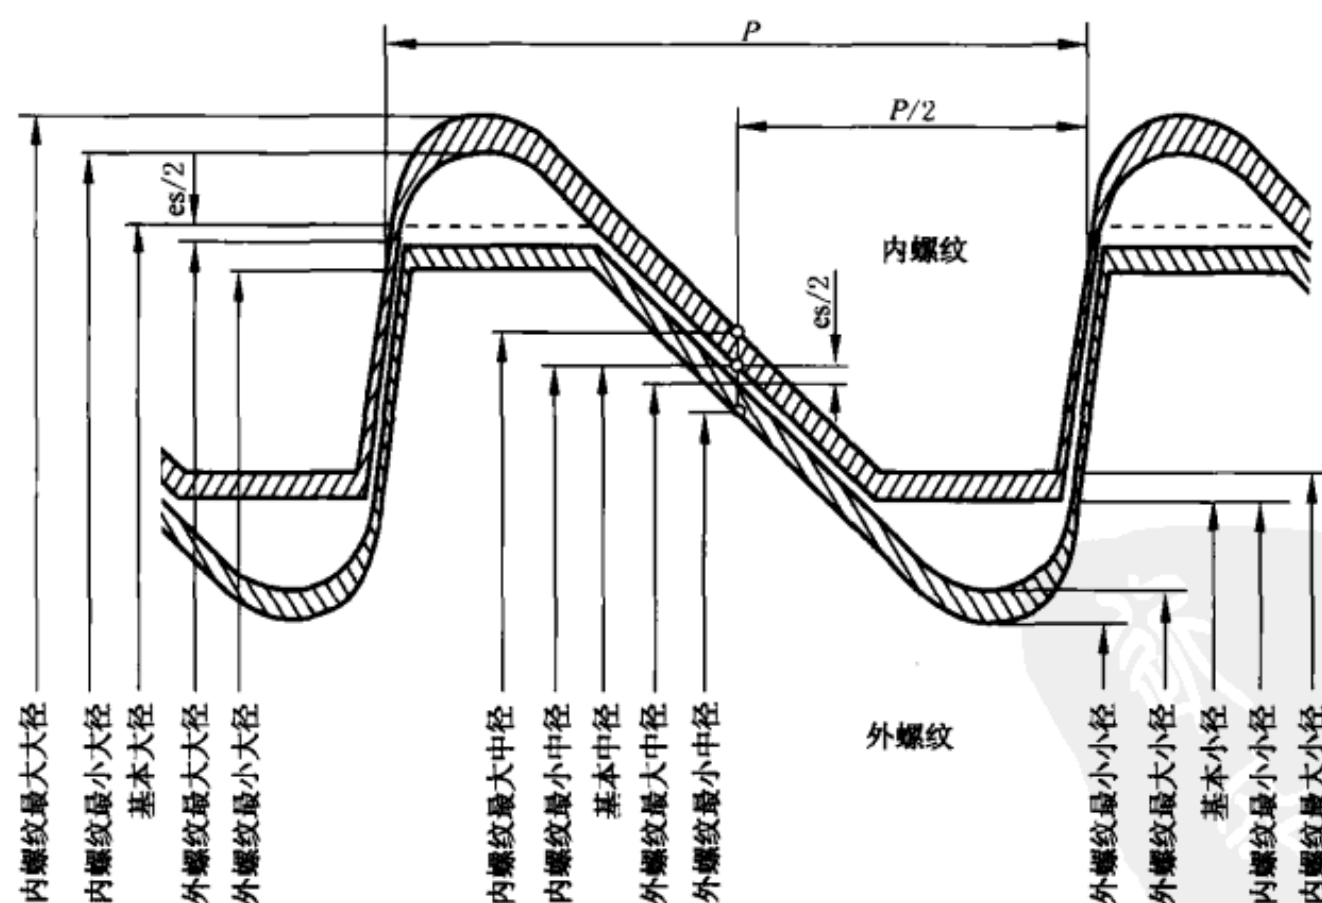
英制锯齿形螺纹的公差带位置
